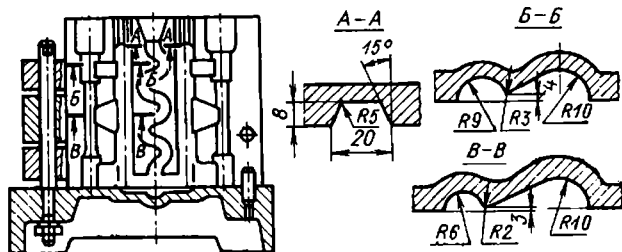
Кокиль с вертикальными подпитывающими бобышками
